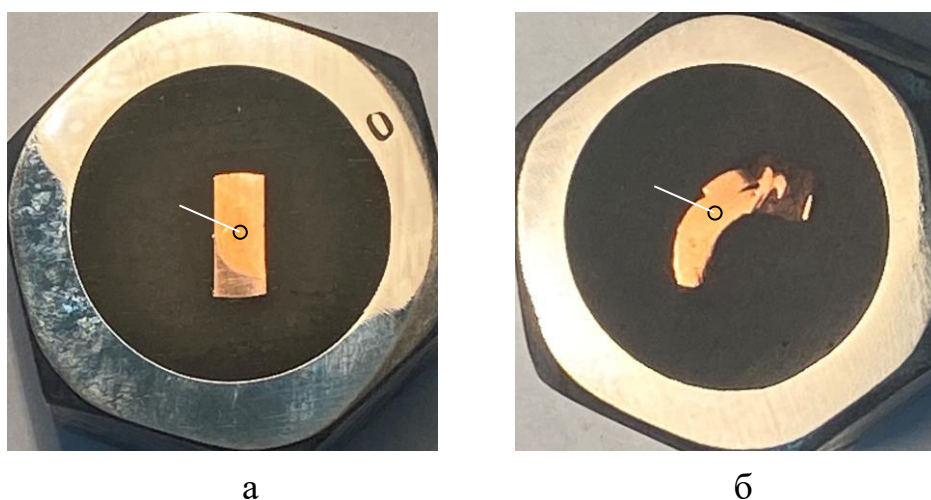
Образцы из медной заготовки после РКУП для измерения микротвердости:
